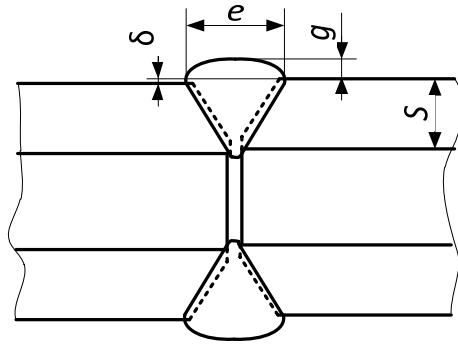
Эскиз стыкового сварного соединения листов
